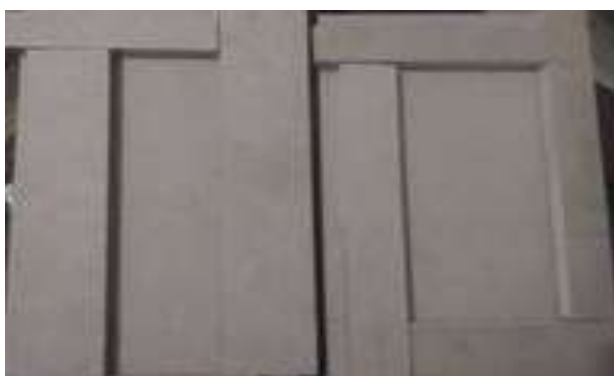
Moldes para probetas de flexión e impacto. [Autor]
